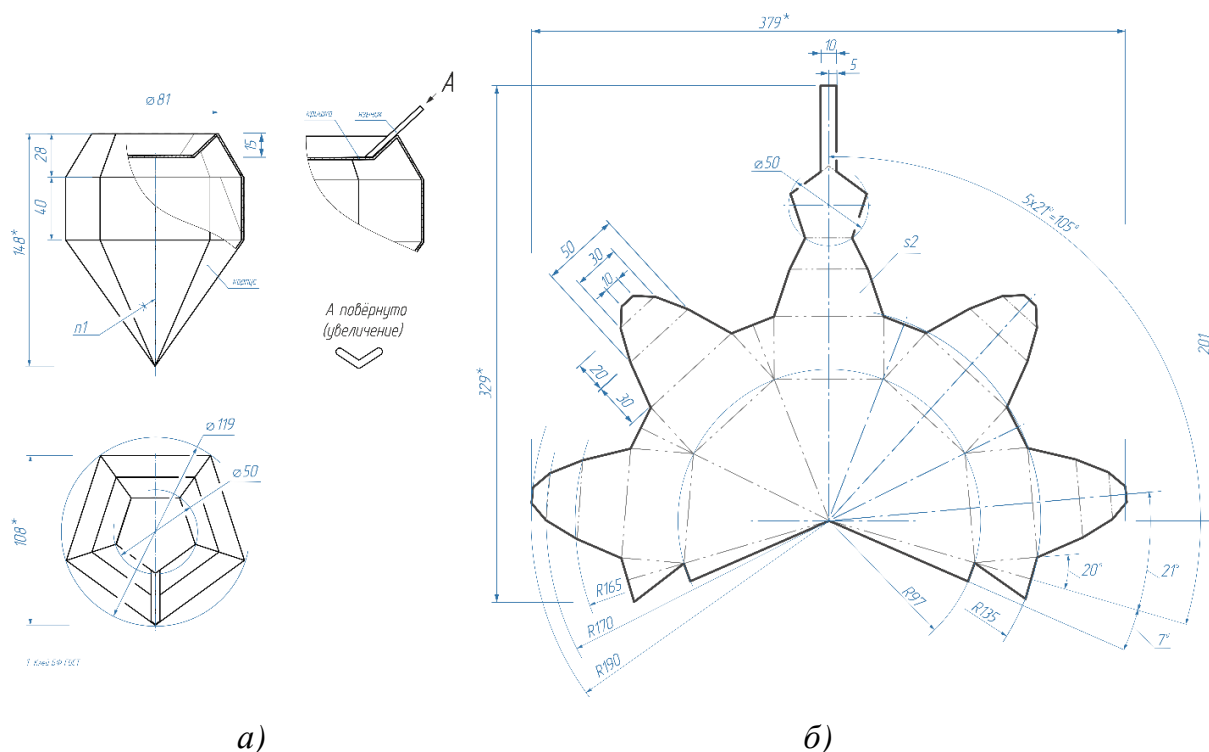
Изображение: а – проекционных чертежей (местный вид, дополнительный вид); б – развертки упаковки
